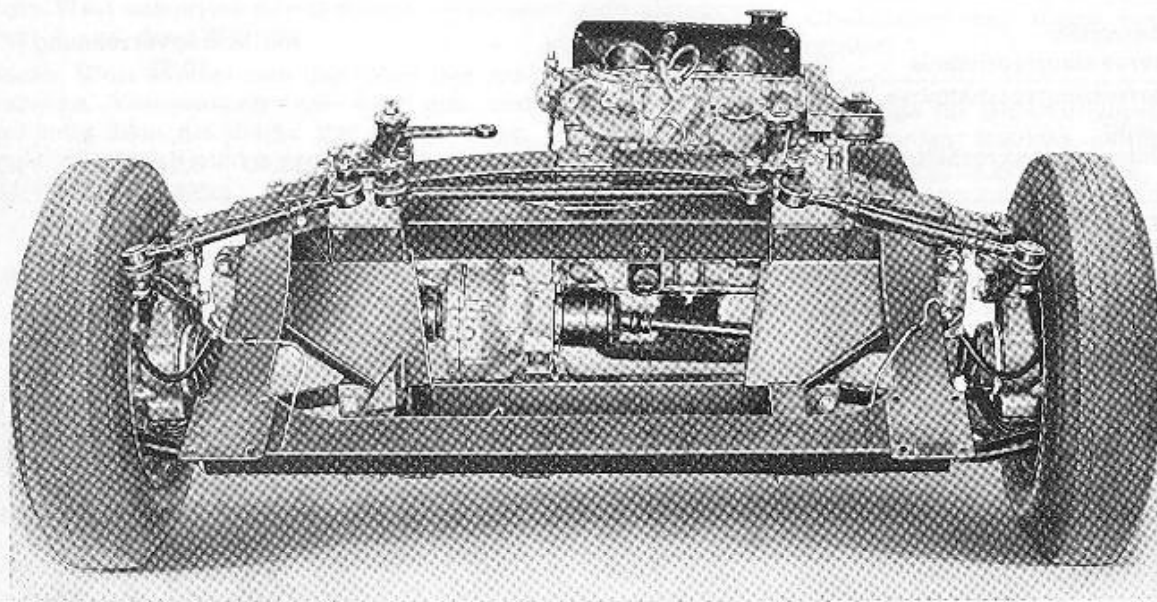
Ansicht der vorderen Radaufhängung und Motoraufhängung von der Rückseite.
